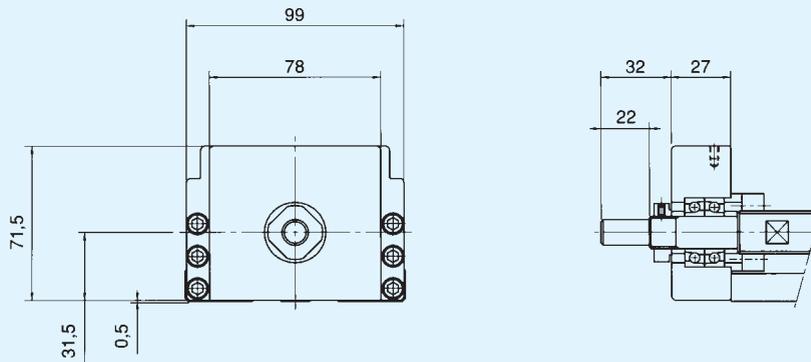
KR55 Housing A ohne Motorflansch (Kennziffer □ □ 10)
